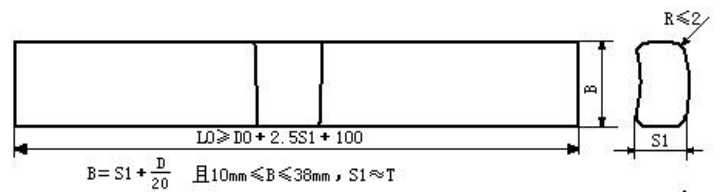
(b) 表 17 注 (2) 焊接位置弯曲试样的截取位置
